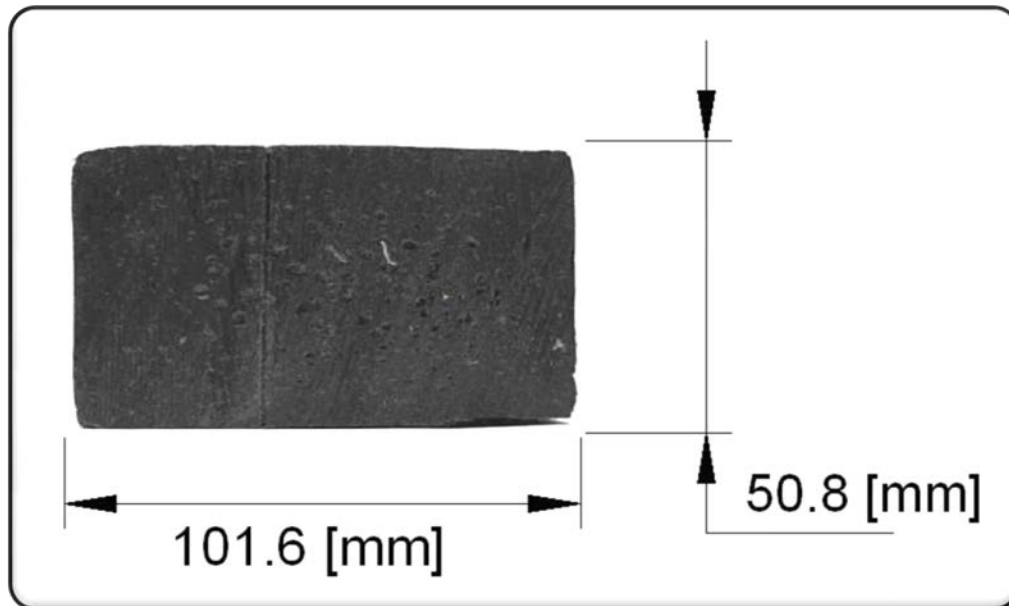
Vista frontal con las dimensiones del perfil BLOK. Tolerancia  $\pm 3$  mm.
